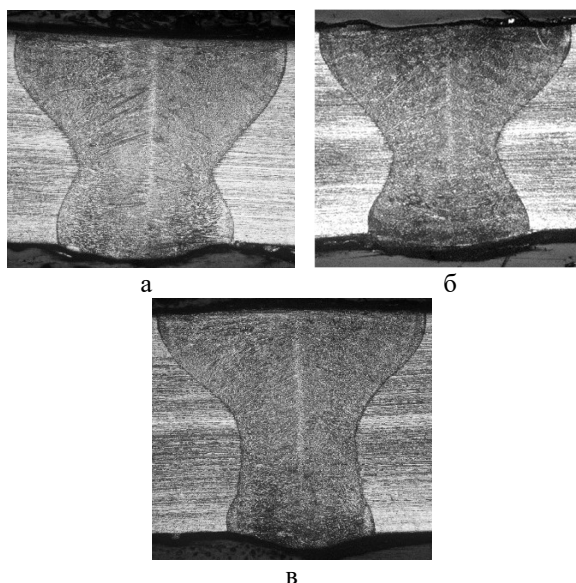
Загальний вигляд стикових зварних з'єднань, $\times 50$: а – Зразок 1; б – Зразок 2, в – Зразок 3
